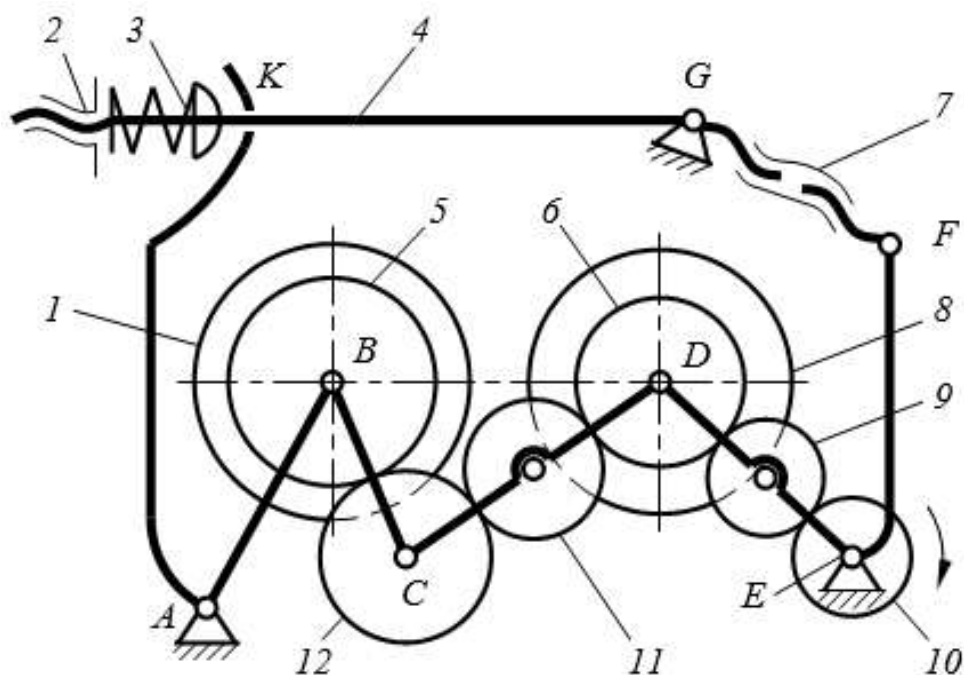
Схема валковой дробилки. 1, 8 – рабочие валы; 2 – винт; 3 – пружина; 4 – тяга; 5, 6, 9, 10, 11, 12 – зубчатые колеса; 7 – винтовой механизм
